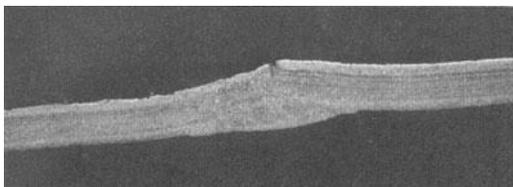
Schlechte Schweißnaht eines Rohres.
